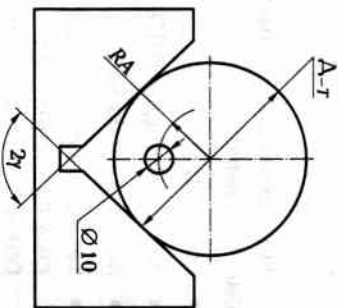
Схема базирования заготовки при сверлении отверстия
